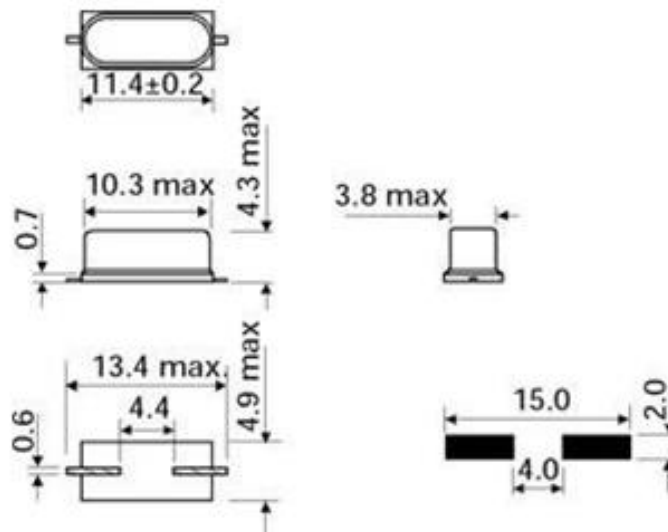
Габаритні розміри корпусу кварцового резонатора
